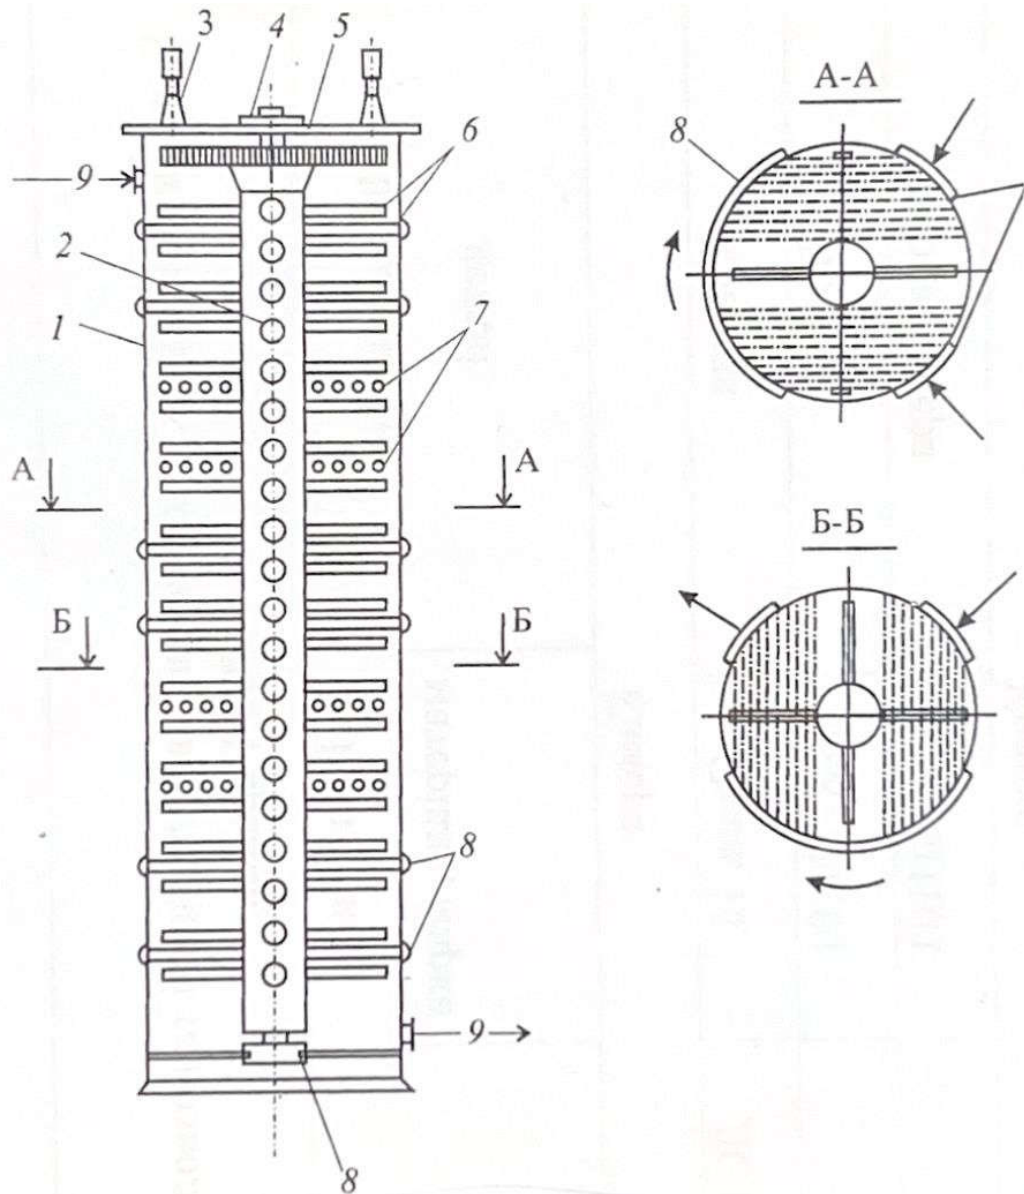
Вертикальний перемішувач-кристалізатор ШІ–ПКВ: 1 – корпус; 2 – трубовал; 3 – привод; 4 – верхня опора; 5 – шестерня; 6,7 – теплообмінні трубки; 8 – колектори; 9 – нижня опора.
